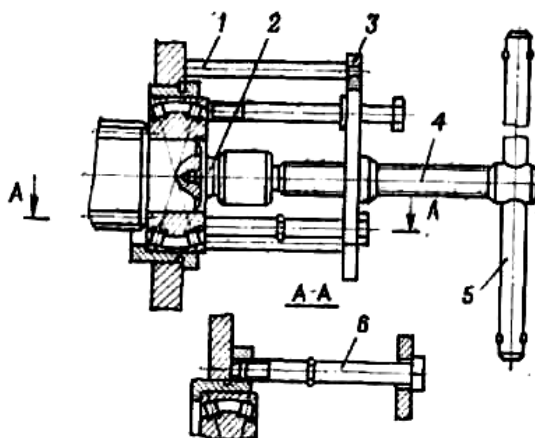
Пристосування для зняття заднього підшипника проміжного вала И-801.31.000: 1 - упор, 2 - наконечник; 3 - плита; 4 - гвинт, 5 - рукоятка; 6 - болт
